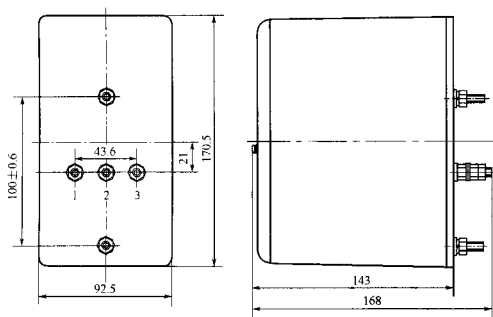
HF2-25 型防护盒的安装尺寸与外形参考尺寸
